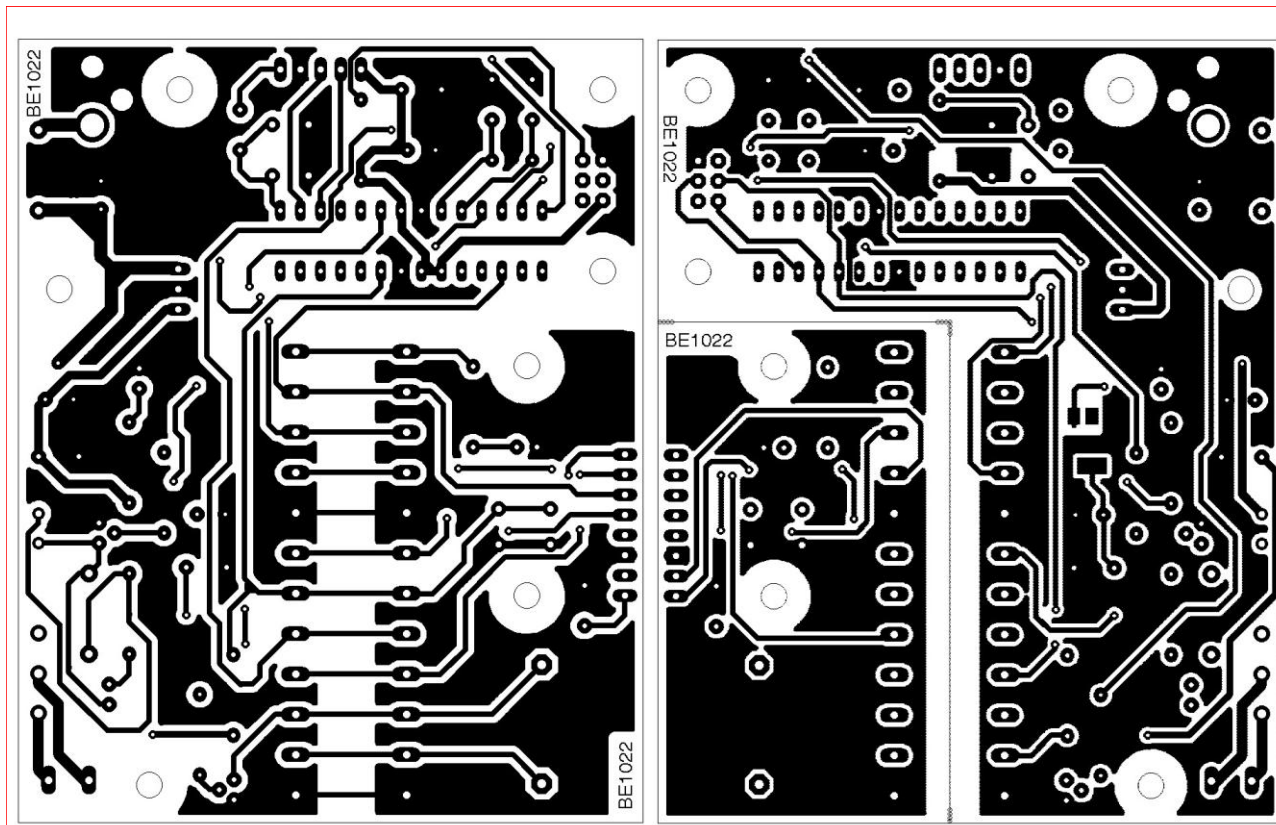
A destra master lato componenti a sinistra master lato saldature.
